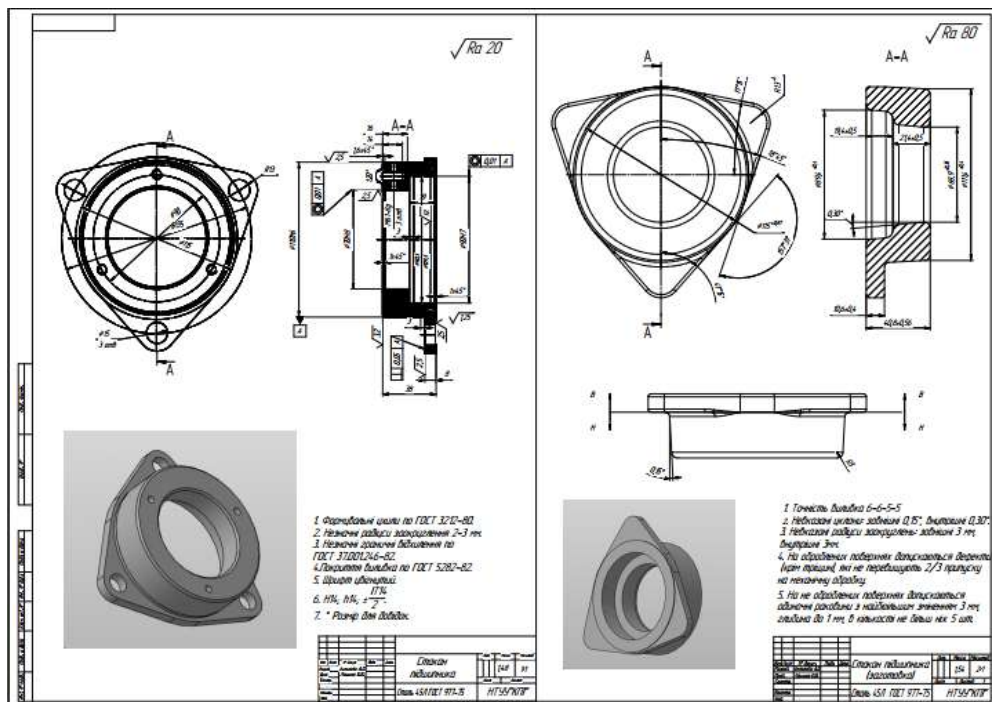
Креслення деталі та заготовки «Стакан підшипника»
